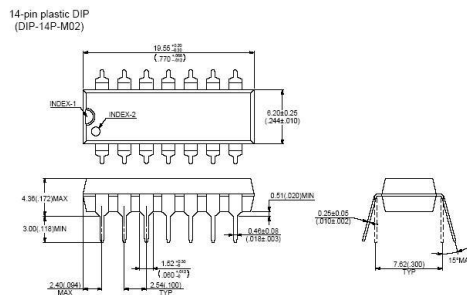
Габаритні розміри мікросхеми CD4026E
